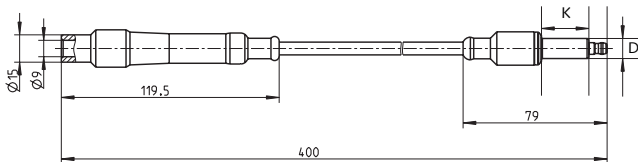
Zündkabelverlängerung Typ 1500A97 (L = 400 mm)
